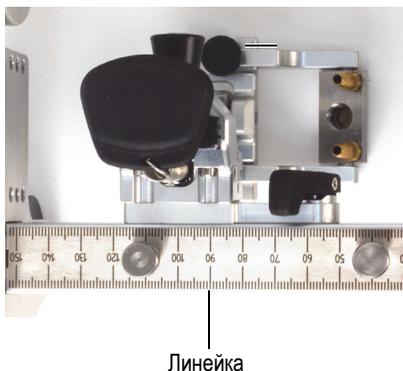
Линейка для настройки положения держателей ПЭП
